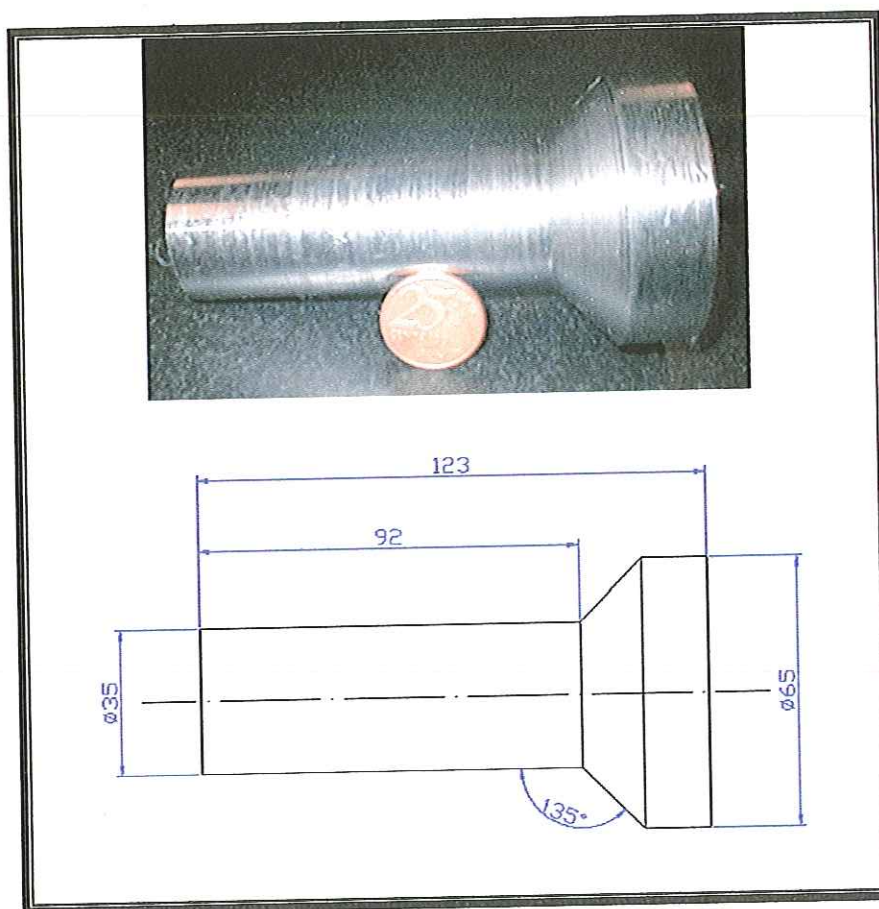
Corpo de prova para impressão do perfil do rebolo após ensaio de desgaste.
